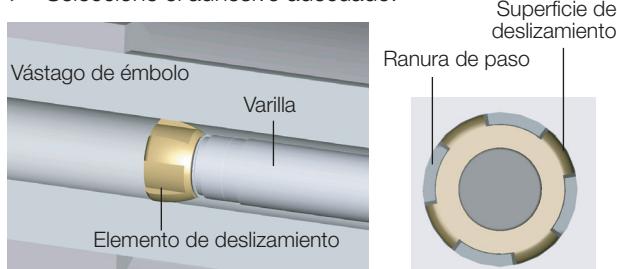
Vista detallada y vista desde arriba del elemento de deslizamiento
